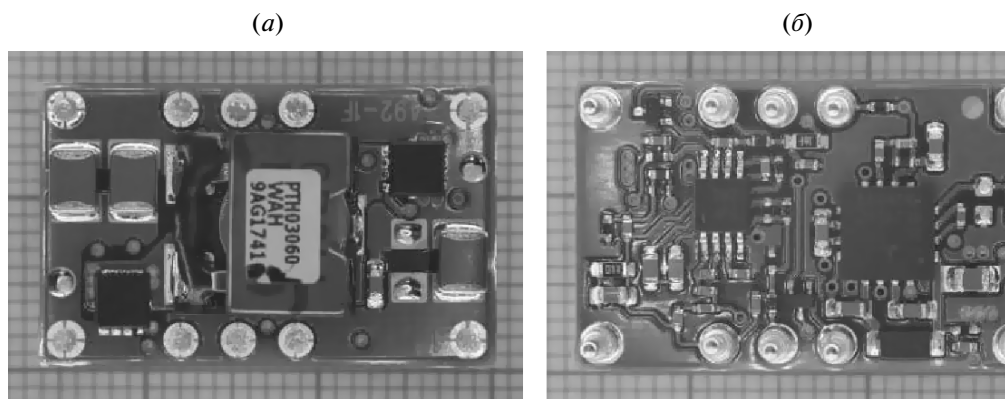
Фотографии образца PTH03060WAN: (а) – вид корпуса сверху, (б) – вид корпуса снизу.
